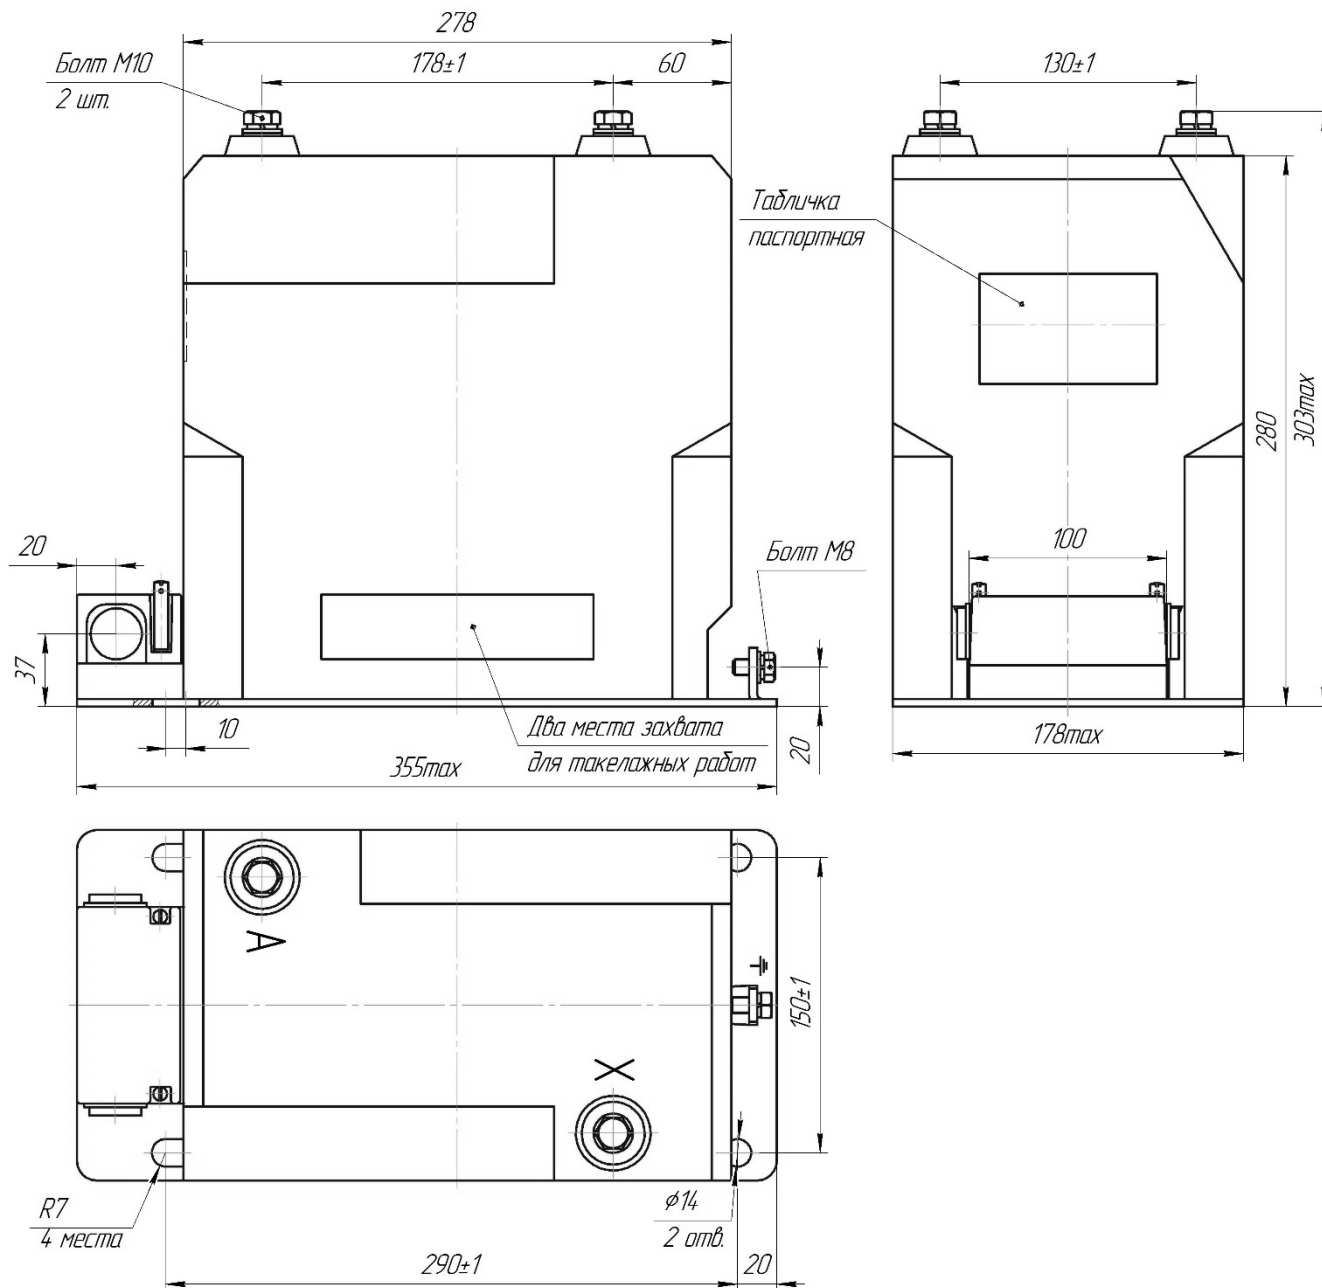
Габаритные, установочные и присоединительные размеры трансформаторов напряжения НОЛ-СЭЩ-6 и НОЛ-СЭЩ-10
